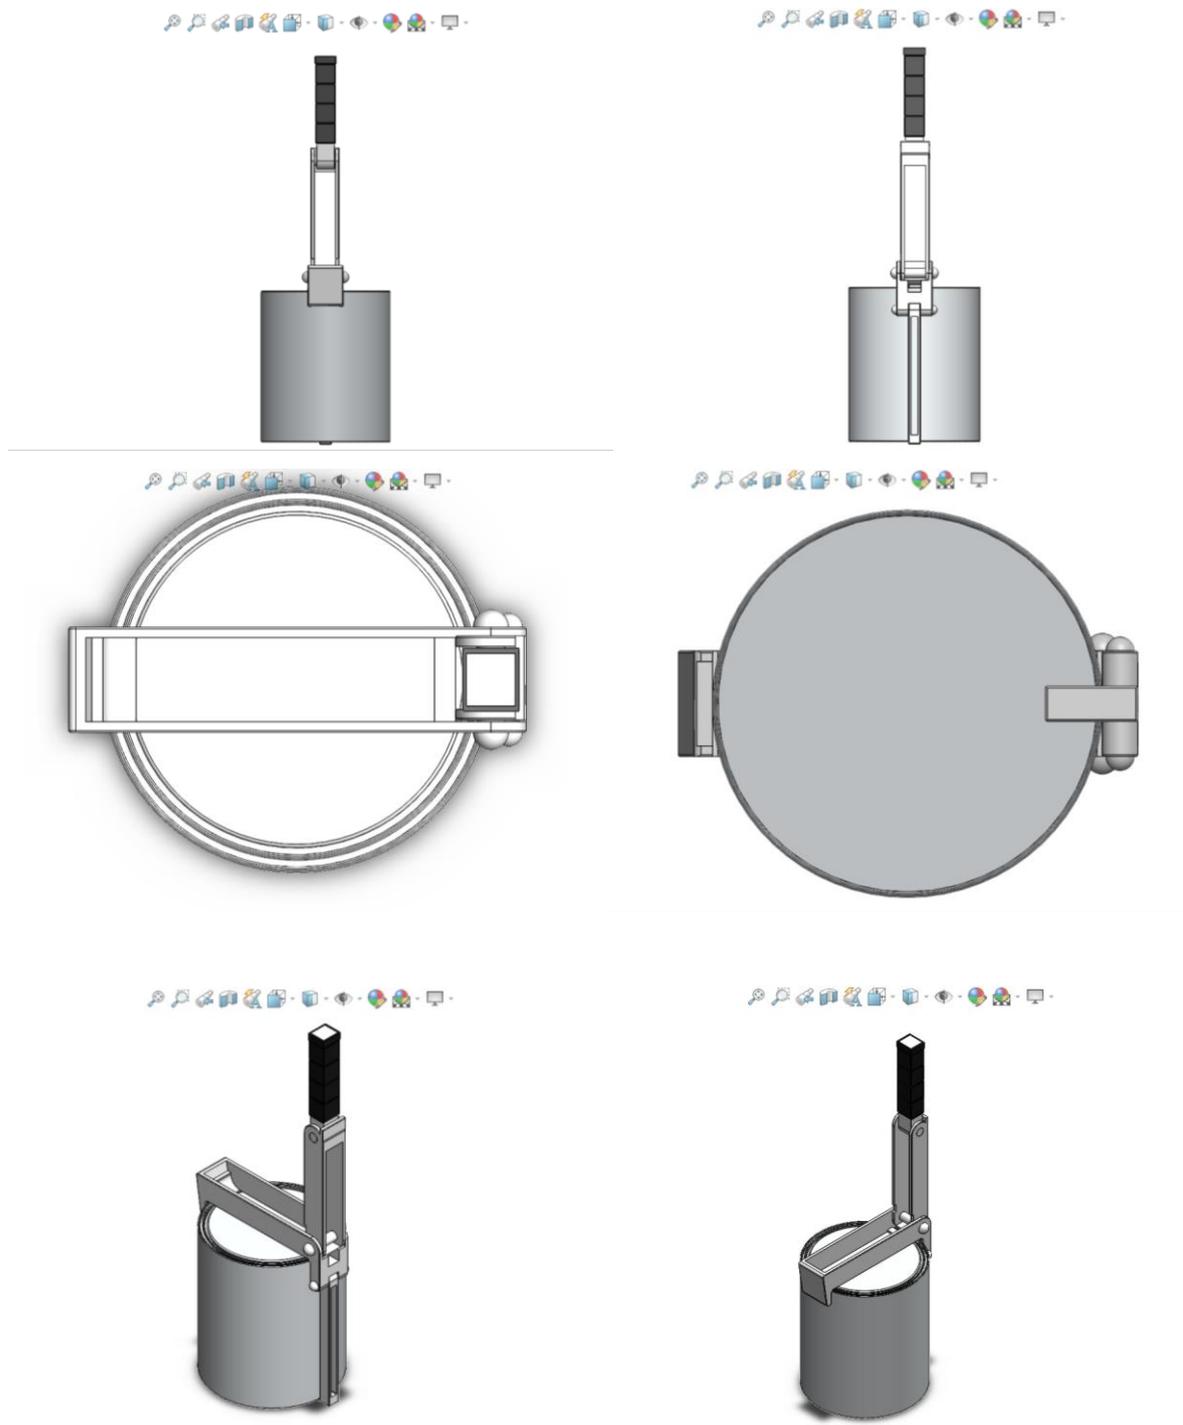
Diseño de abrelatas mecánico para botes de pintura (diferentes vistas).
